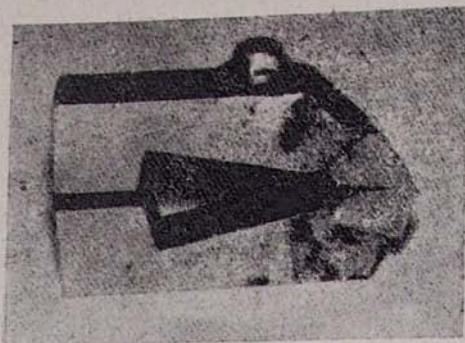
Специальный резец со спаянными пластинками из сплава ВК8 и Т15К6.
